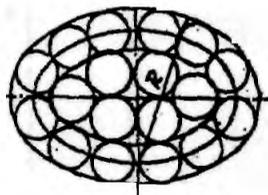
Схема секторной токопроводящей жилы силового кабеля сечением 25-70 кв.мм (до уплотнения)
